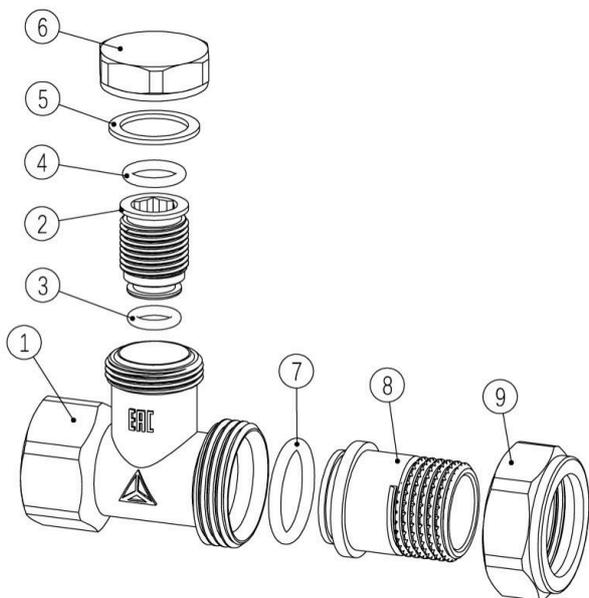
Клапан радиаторный запорно-регулирующий прямой
